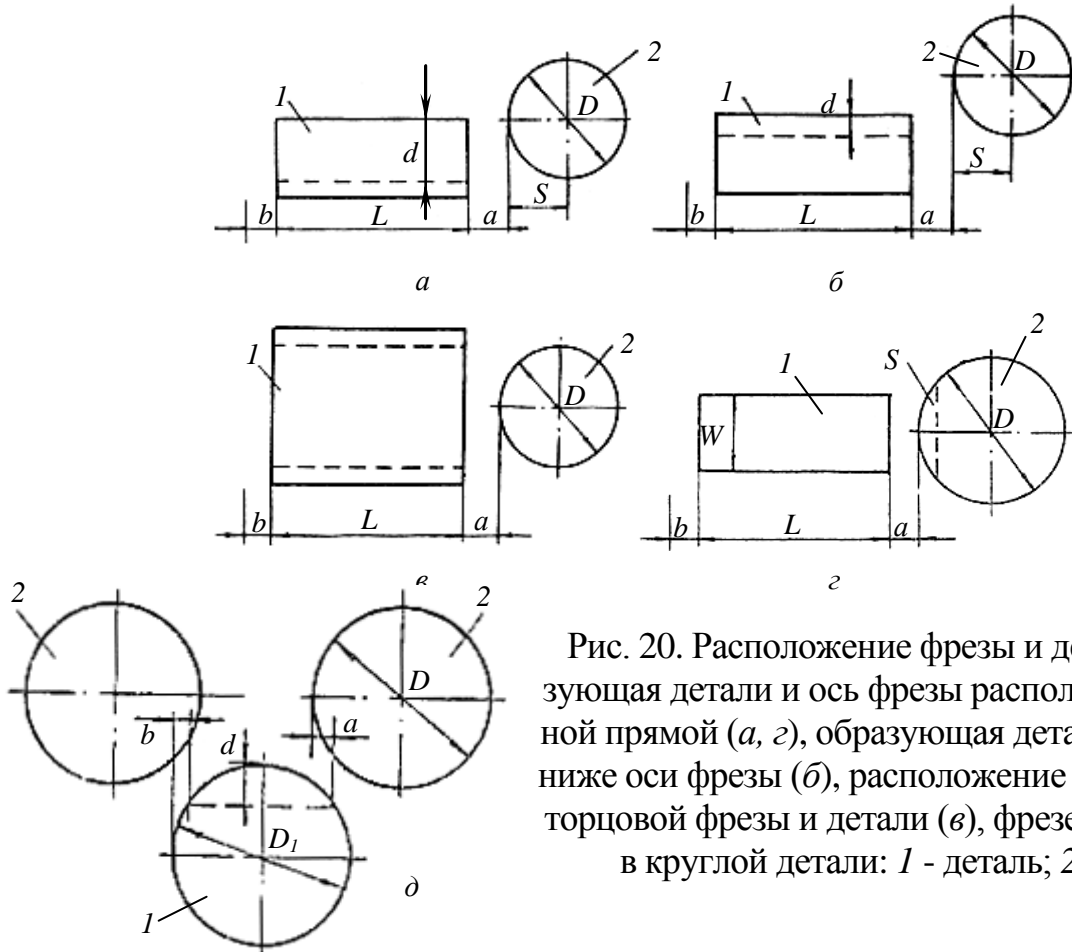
Расположение фрезы и детали: образующая детали и ось фрезы расположены на одной прямой (а, в), образующая детали находится ниже оси фрезы (б), расположение концевой или торцевой фрезы и детали (в), фрезерование паза в круглой детали: 1 - деталь; 2 - фреза
